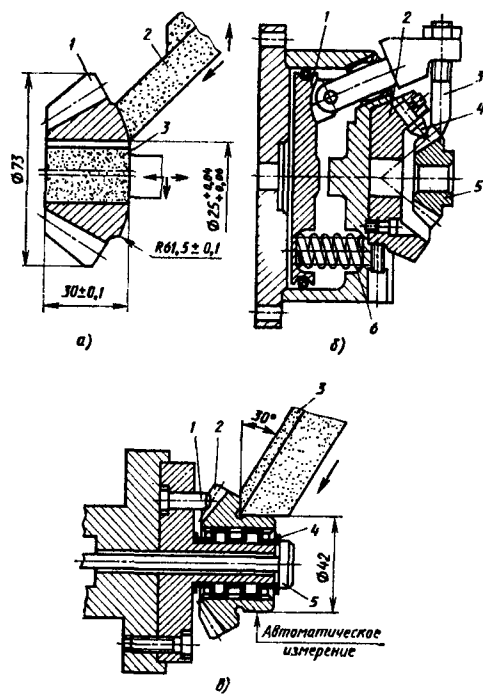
Схемы установки прямозубых конических колес в зажимных приспособлениях при шлифовании базовых поверхностей
